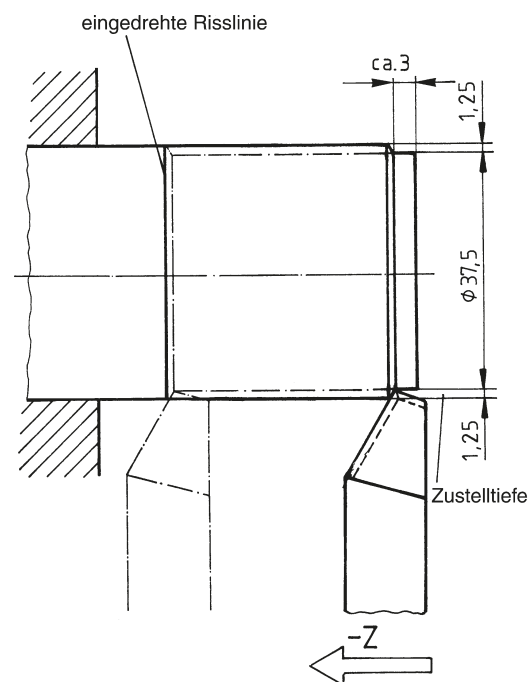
Werkstück mit markierter Drehlänge und angedrehtem Durchmesser
